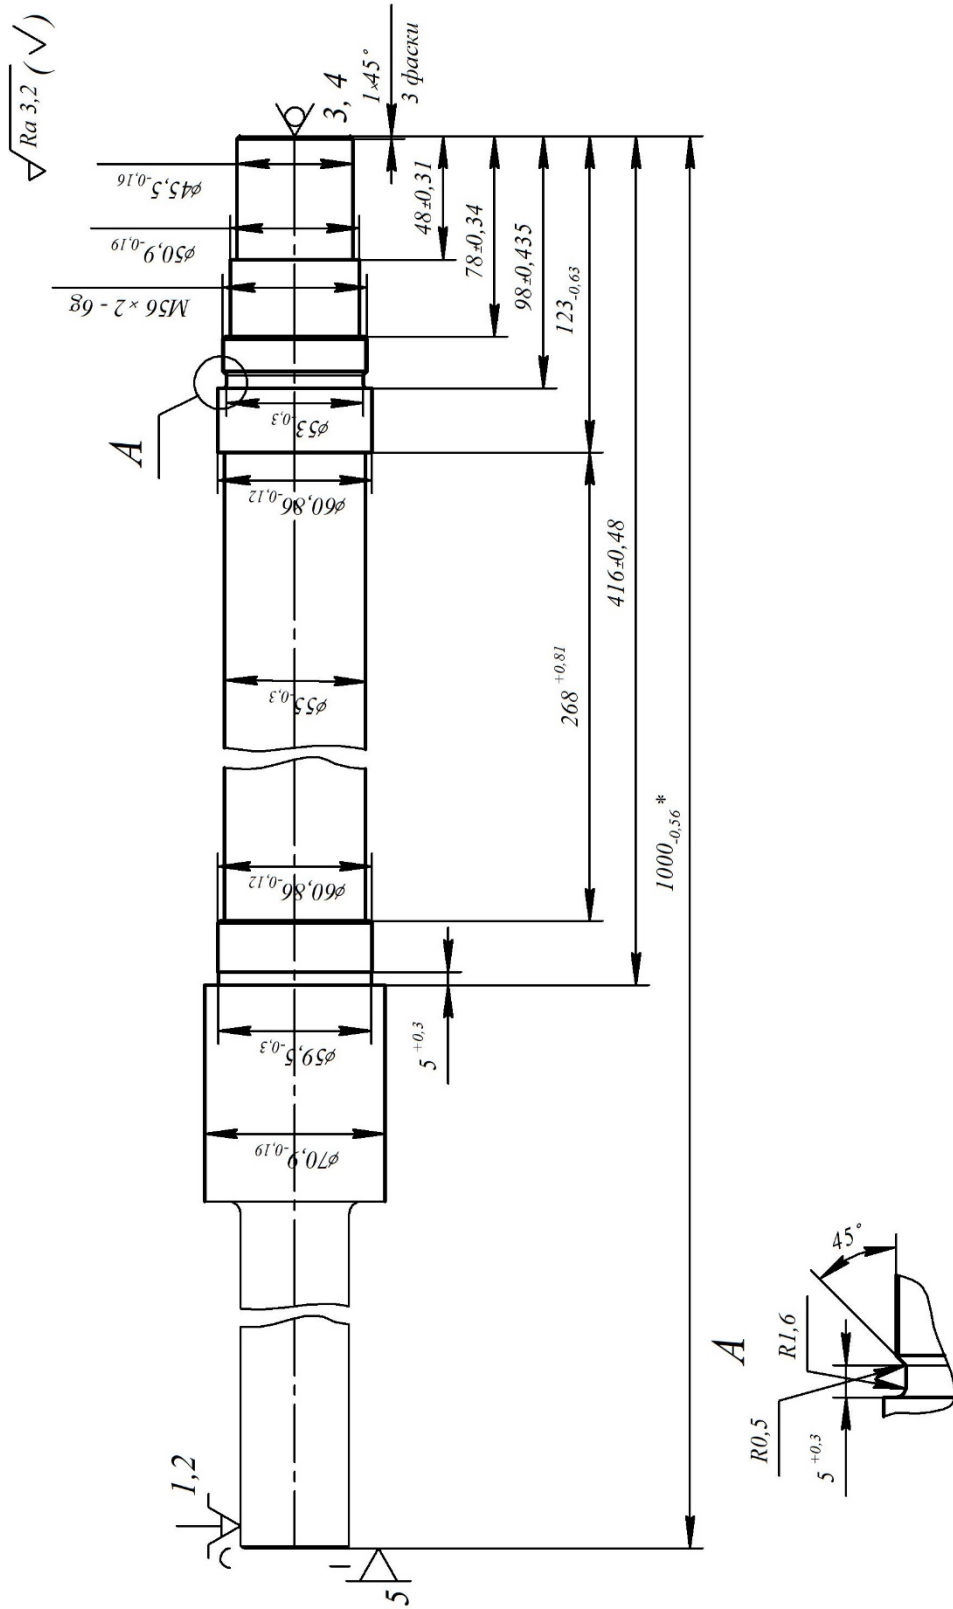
Альтернативна схема базування заготовки на операції токарній 025, установ А
